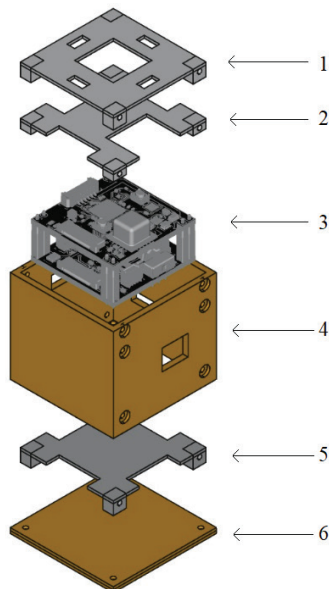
Аппарат *PocketQube*. Модель конструкции: 1 – крышка; 2 – защитная пластина аккумулятора; 3 – электроника аппарата; 4 – основа корпуса; 5 – защитная пластина аккумулятора; 6 – нижняя защитная пластина
